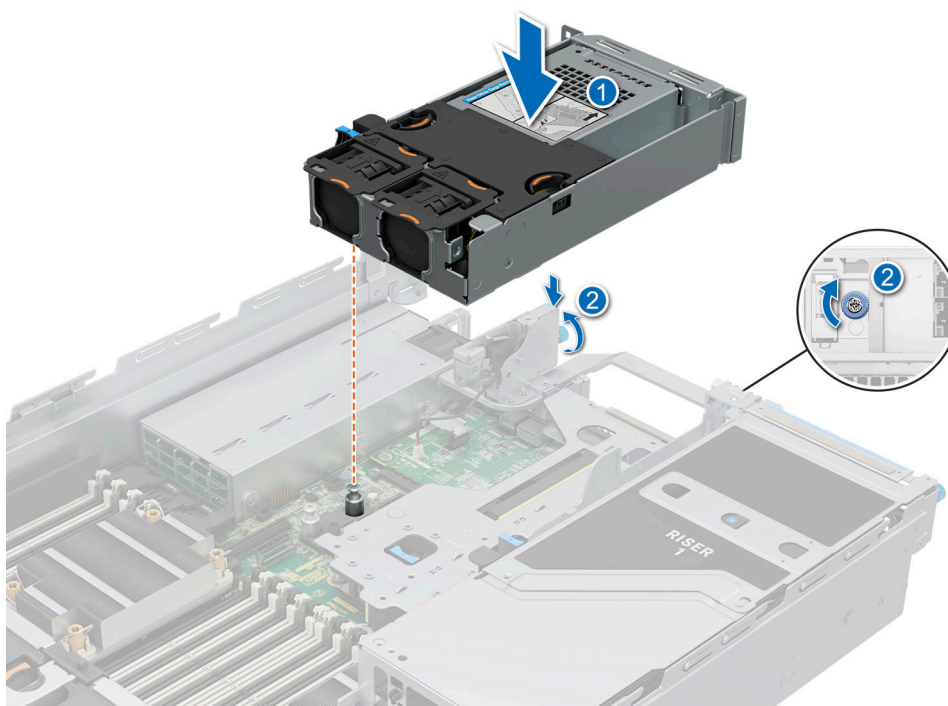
Installation du module de disques arrière 2 x 2,5 pouces
